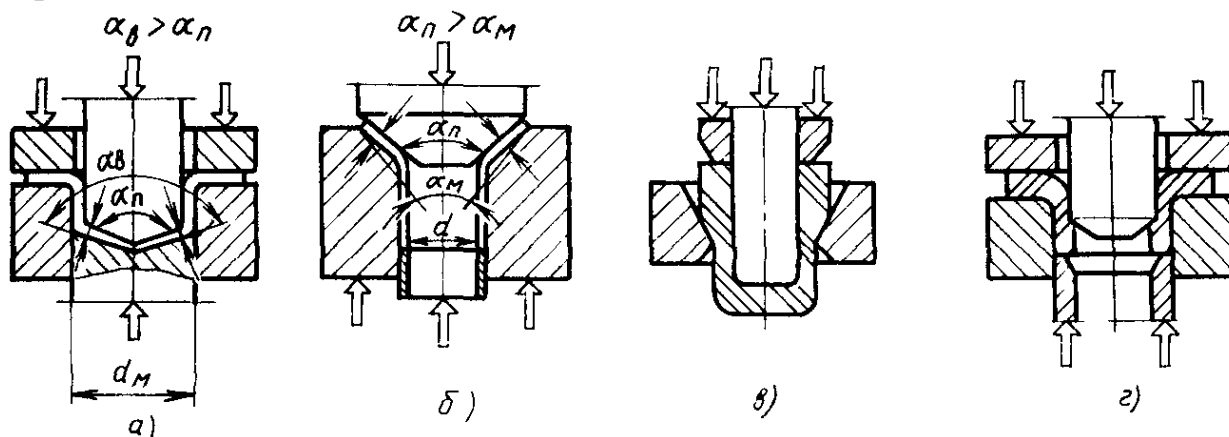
Схема дополнительного силового воздействия на заготовку при: а — отбортовке; б — раздache; в — вытяжке с утонением; г — отбортовке с утонением
